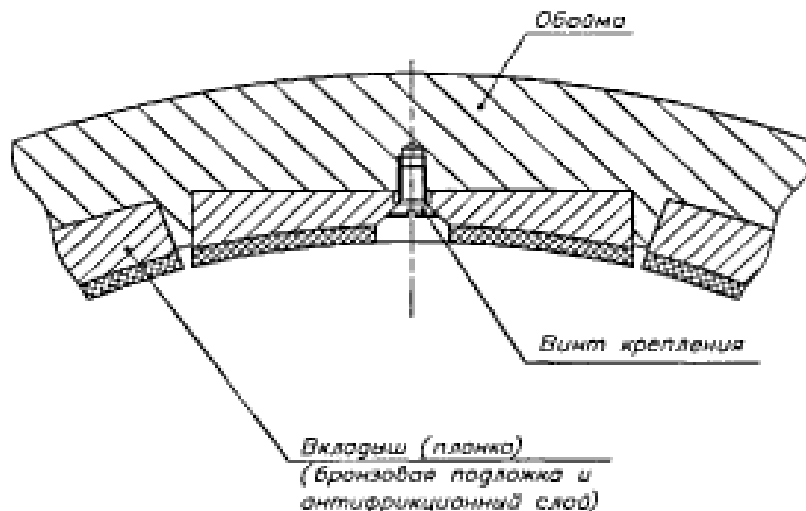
Исполнение сегментного бронзофторопластового подшипника
